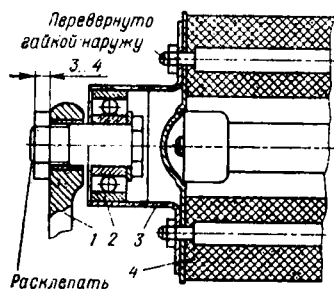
Соединительная муфта в сборе с педалью и шатуном:
